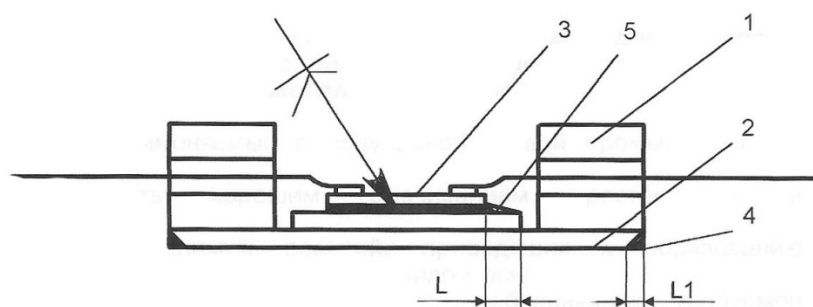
Приклейка подложки на основание корпуса с планарными выводами: 1 - основание корпуса; 2- нижняя крышка корпуса; 3- подложка; 4- сварной шов; 5 - дефект при приклейке (попадание клея в "запретную" зону); L, L1 - зоны под сварку и герметизацию
